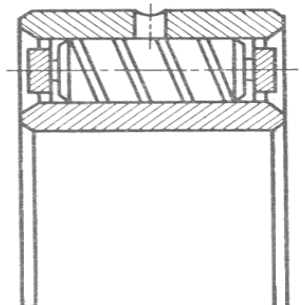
Радиальный роликовый подшипник с витыми роликами
